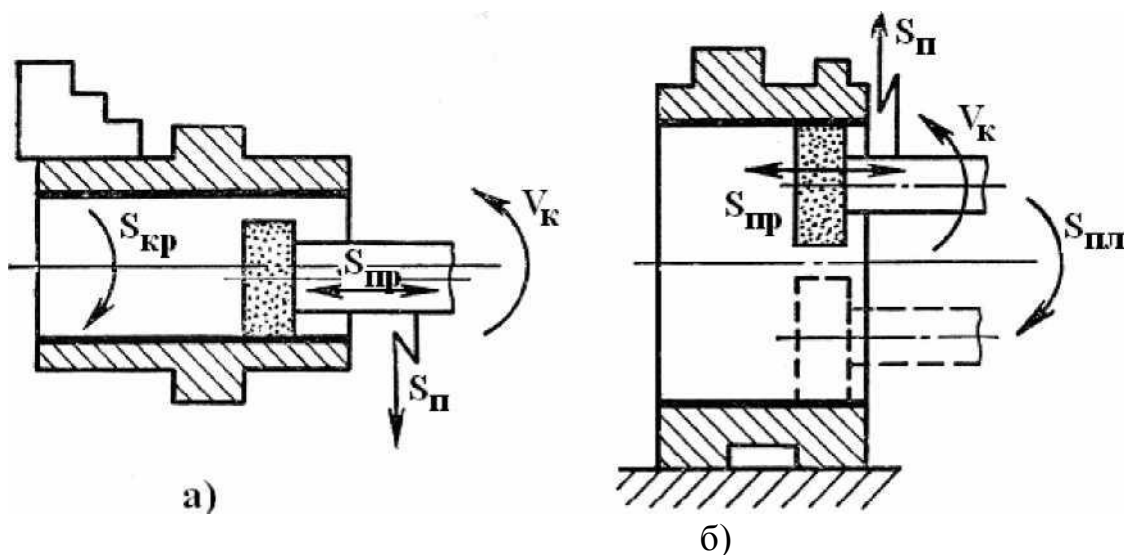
Схемы обработки заготовок на внутришлифовальных станках: а - закрепление заготовки в патроне; б - планетарное шлифование
